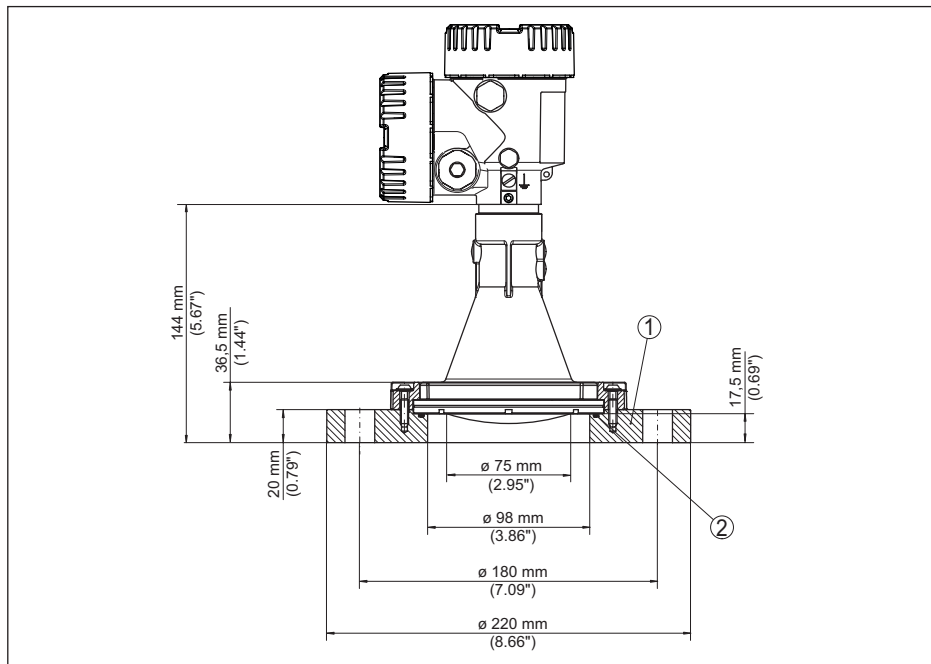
NCR-86 com flange adaptador DN 100 PN 6
